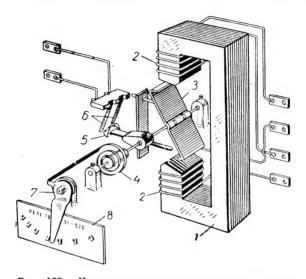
Конструкция реле максимального тока: 1 — сердечник; 2 — обмотки; 3 — якорь; 4 — пружина; 5 — контактный мостик; 6 — контактные пружины; 7 — стрелка-указатель; 8 — шкала.
